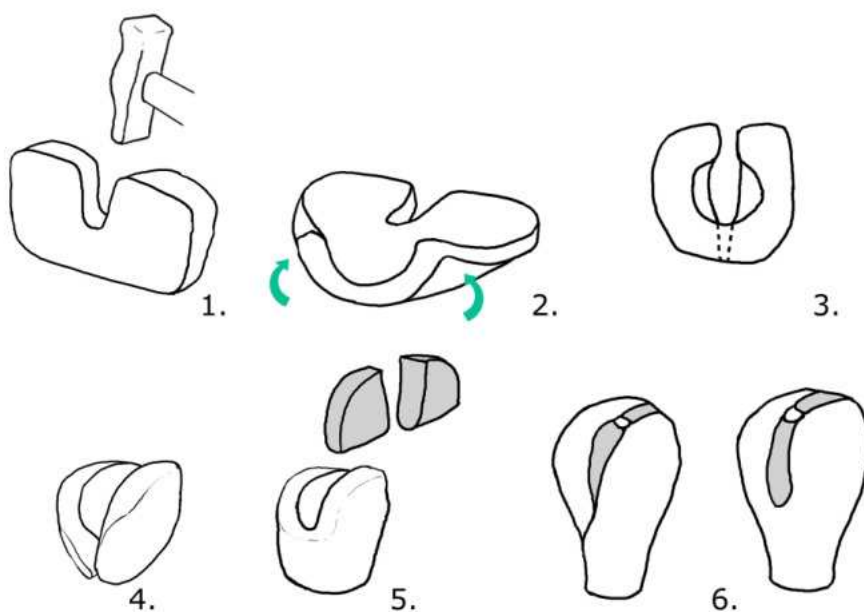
Procédé par pliage et soudage avec insert. Dessin F. Cognot.
